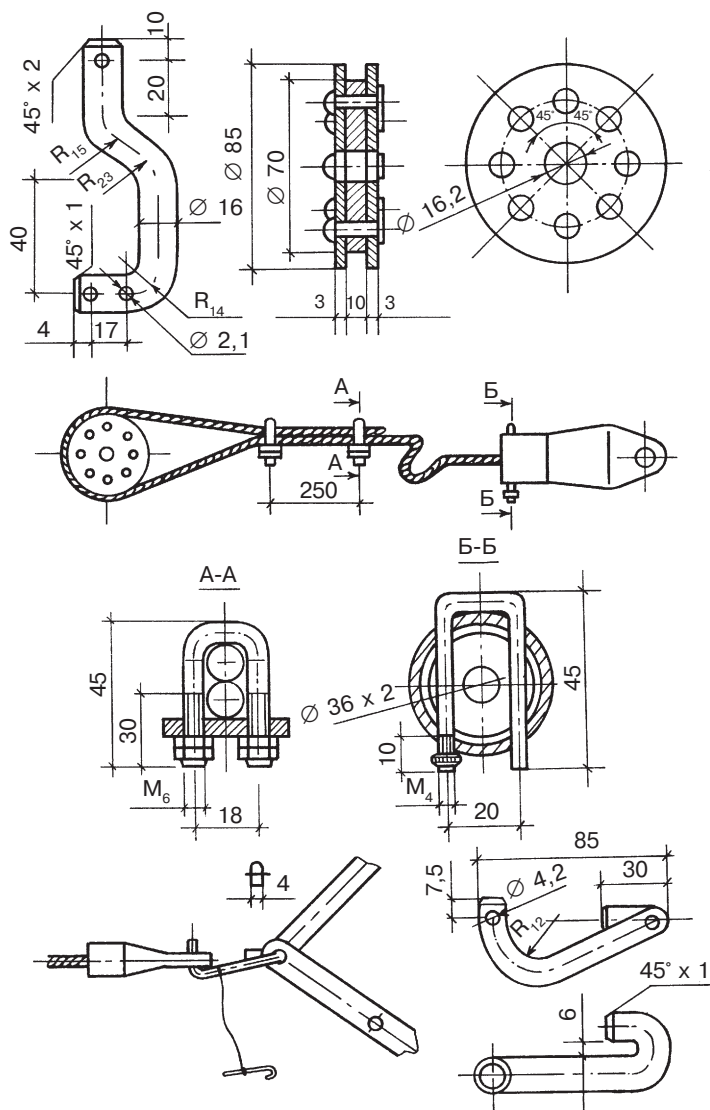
(продолжение). Чертежи для изготовления деталей и узлов двигателя для мини-ГЭС
